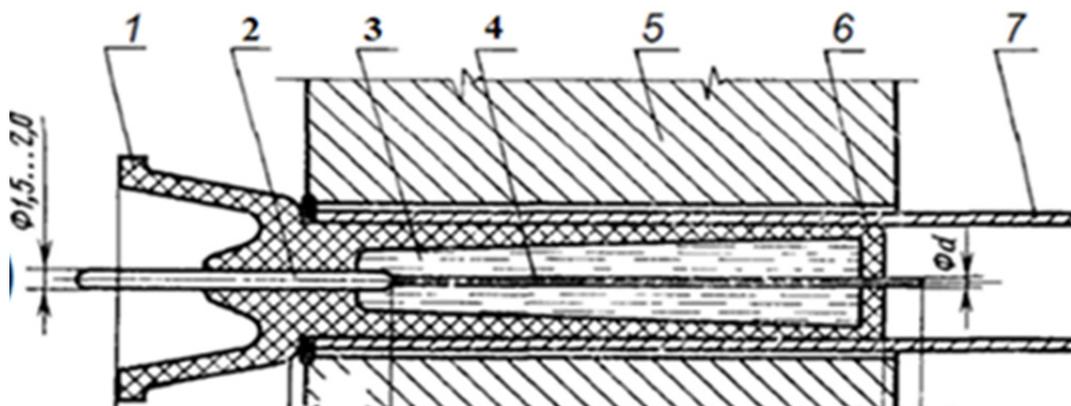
Конструкция электровзрывного картриджа: 1 – корпус патрона; 2 – токопроводящая часть проводника; 3 – наполнитель (передающая среда); 4 – взрывающаяся часть проводника; 5 – трубная решетка; 6 – заглушка (торцевая пробка); 7 – труба
